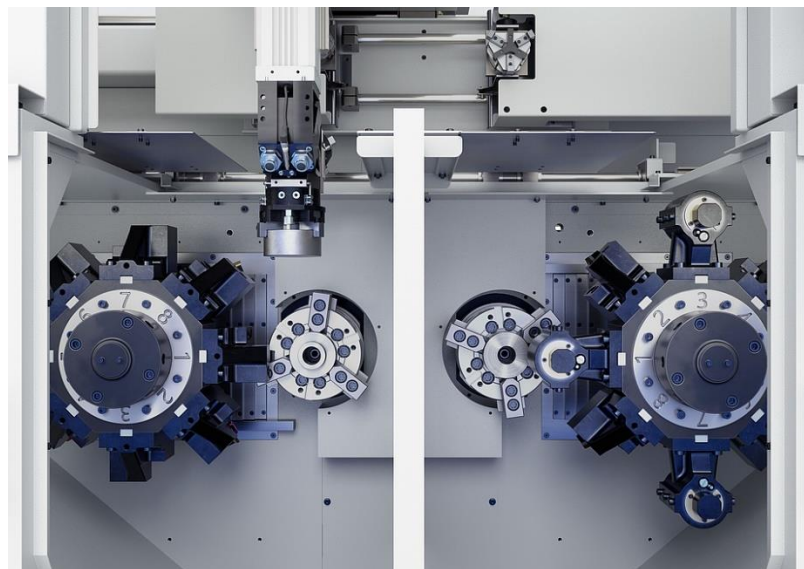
Робоча зона токарного верстата з ЧПК MSC 5 DUO
